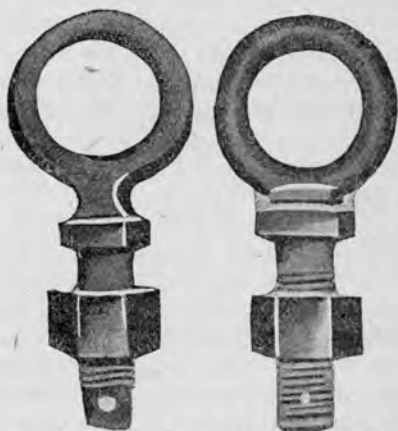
Разрушение железных частей чугунного трубчатого колодца с грунтовой водой.
